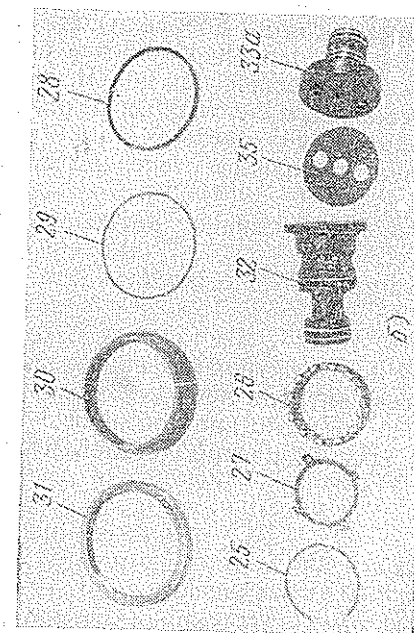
Детали винта АВ-2 для установки на вал редуктора двигателя.
